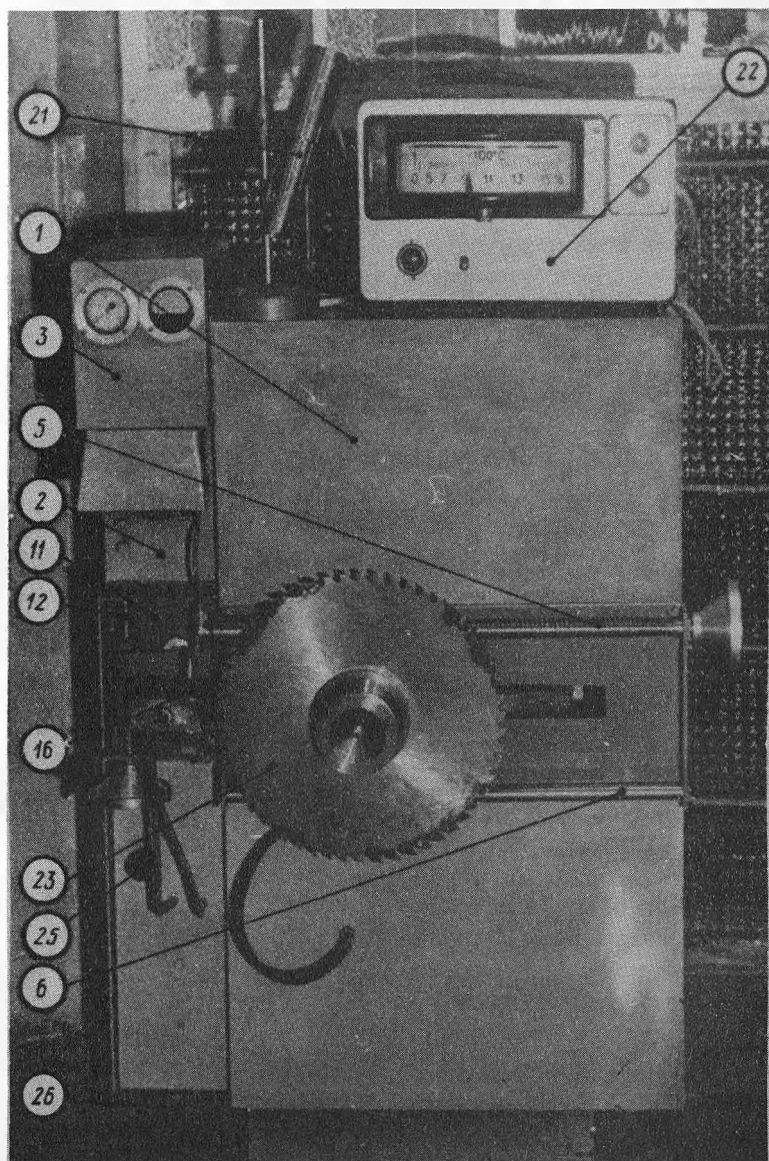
Общий вид станка с приспособлением для бесконтактного контроля температур.
